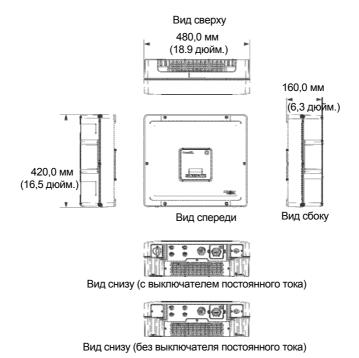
Внешний вид и размеры инвертора Conext RL 3000 E-S/ 3000 E
